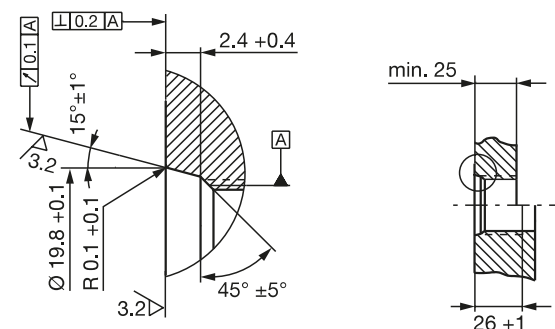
Einschraubloch M18x1.5 nach ISO 6149 O-Ring 15.4x2.1
